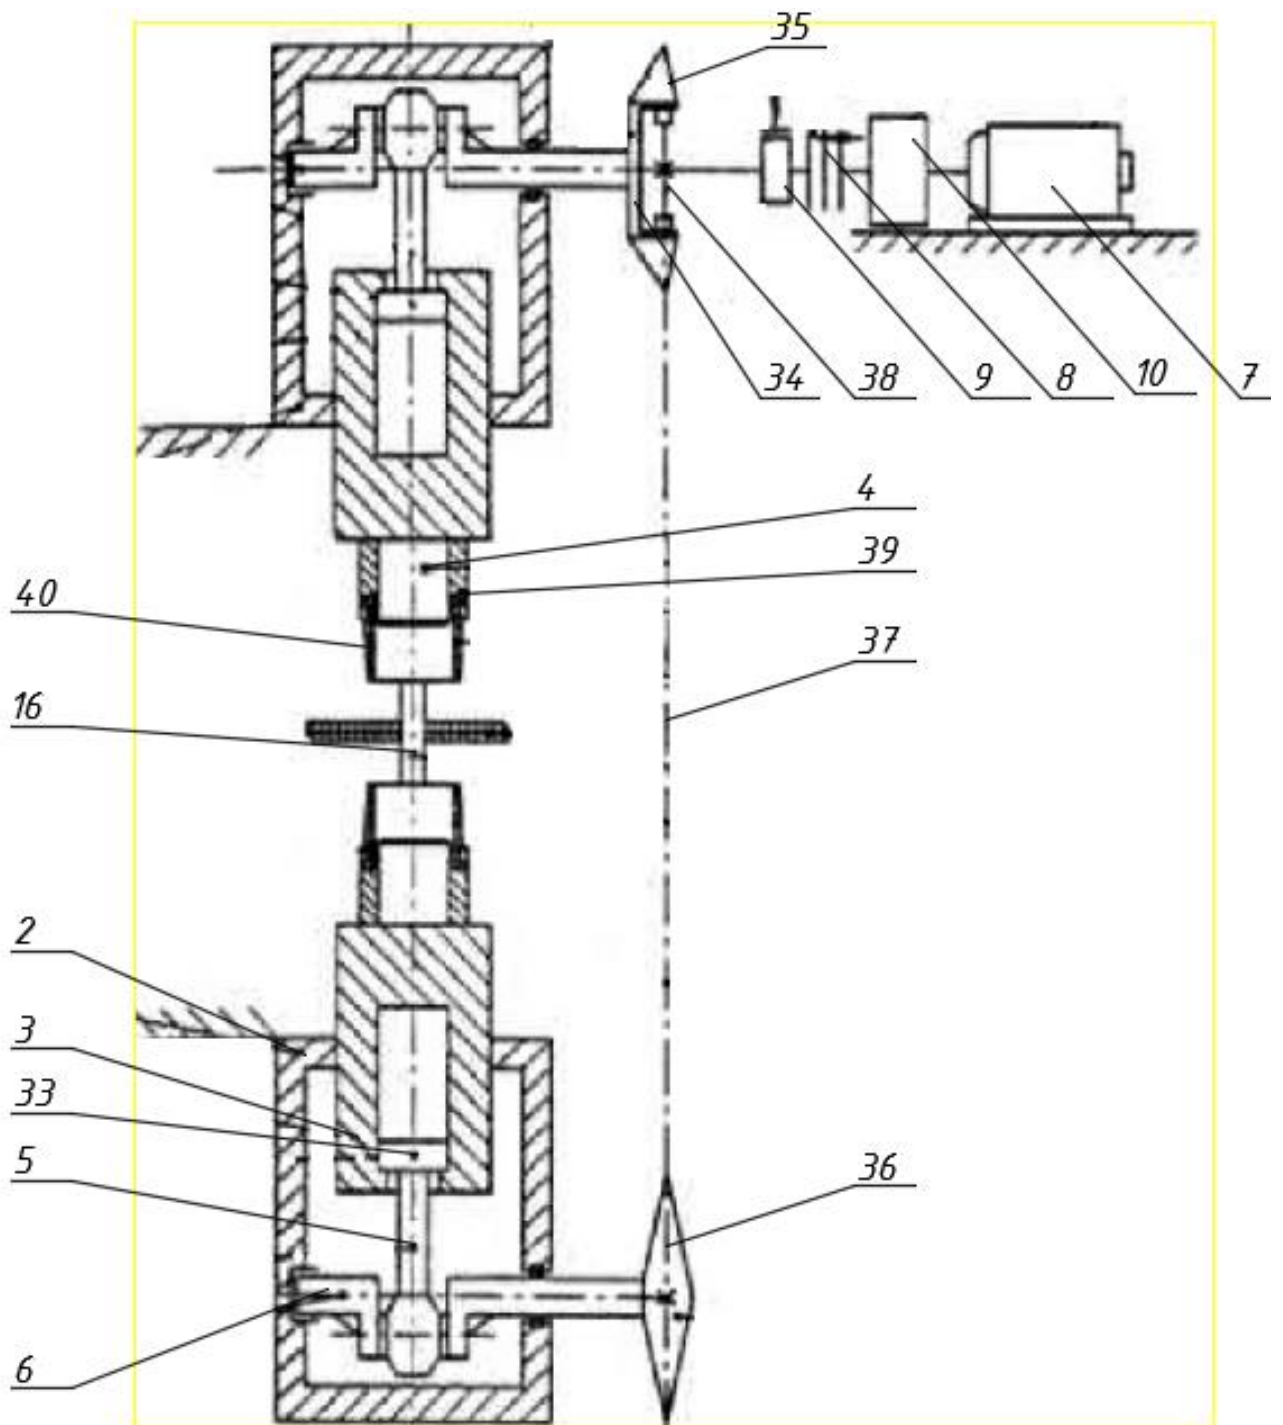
Високошвидкісна машина для обробки металів тиском
